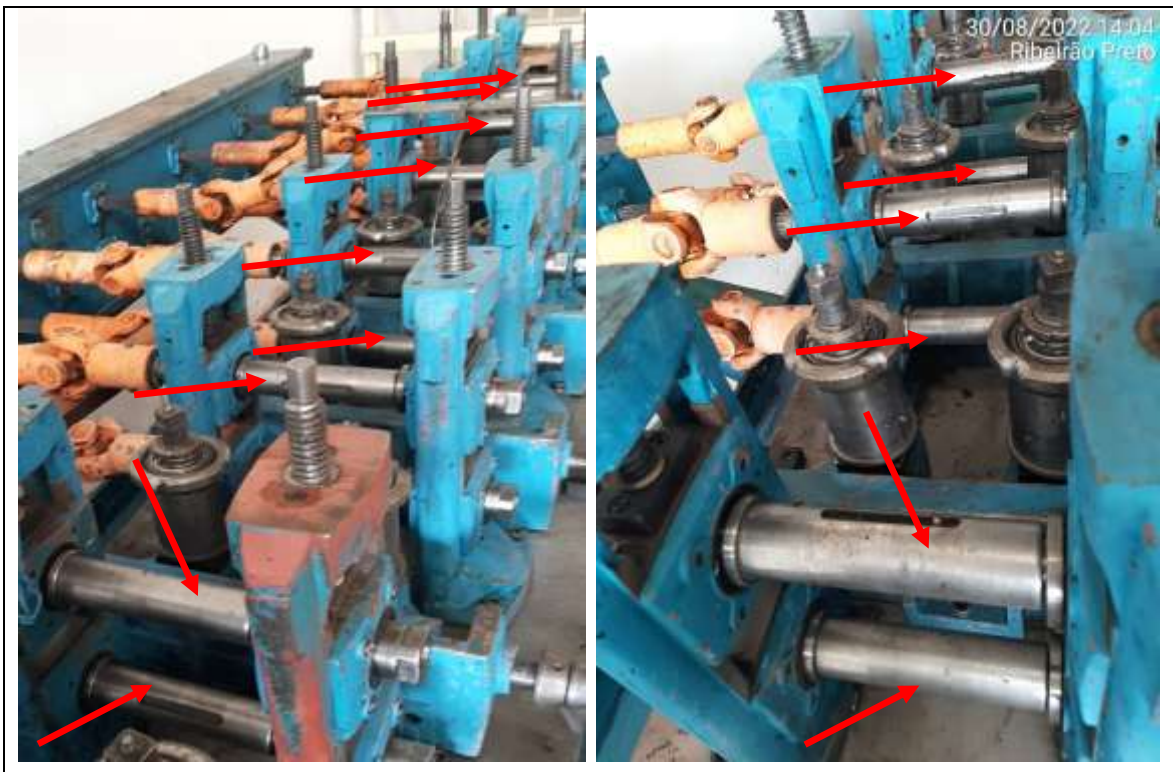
e 14 – Estrutura relativa à calibração dimensional do Tubo de aço após Conformação e soldagem, para o término do processo contínuo de conformação à frio, constando 03 mancais de posicionamento dos conjuntos de Rolos Calibradores acionados por motor elétrico marca WEG desacoplado da máquina, e conjuntos de cardans com o acoplamento de acionamento (foto 14).
